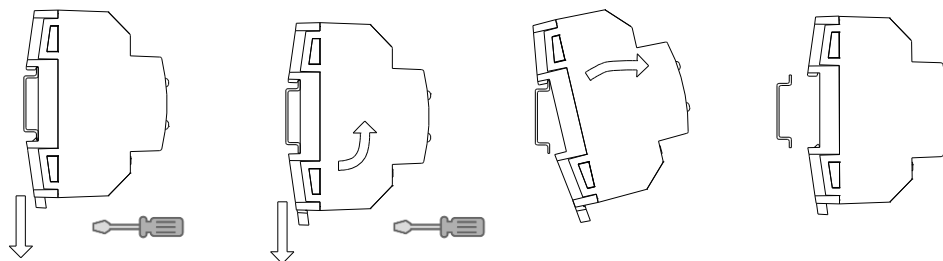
Montaje de MAXinBOX 24 en carril DIN
